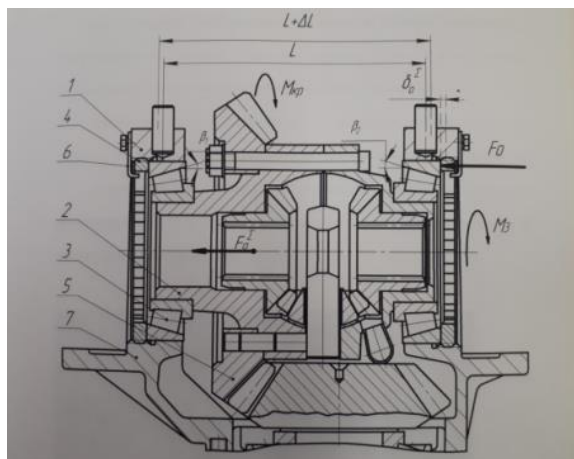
Конструктивная схема дифференциала редуктора в сборе с ведомой шестерней и подшипниками. 1 – крышка, 2 – чашка дифференциала, 3 – конический подшипник, 4 – резьбовое корончатое регулировочное кольцо, 5 – ведомая шестерня, 6 – стопорный элемент регулировочного кольца, 7 – картер редуктора
